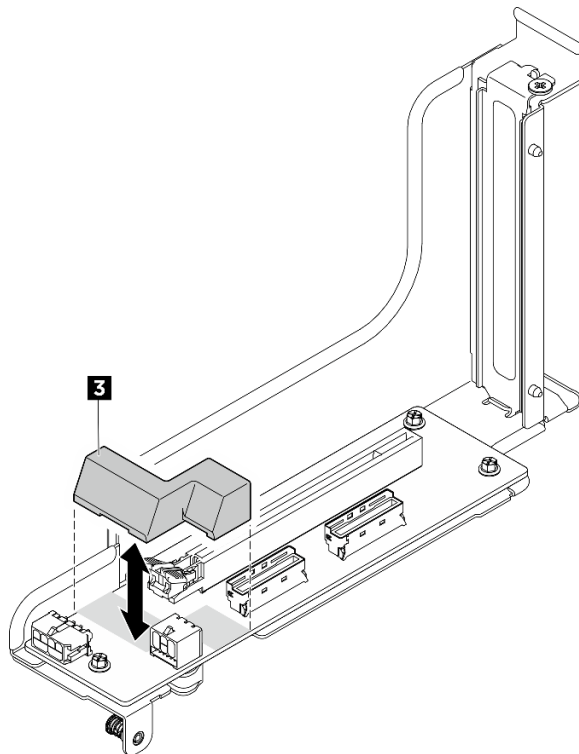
Entfernen der DPU-Luftführung von der PCIe-Adapterkarte
